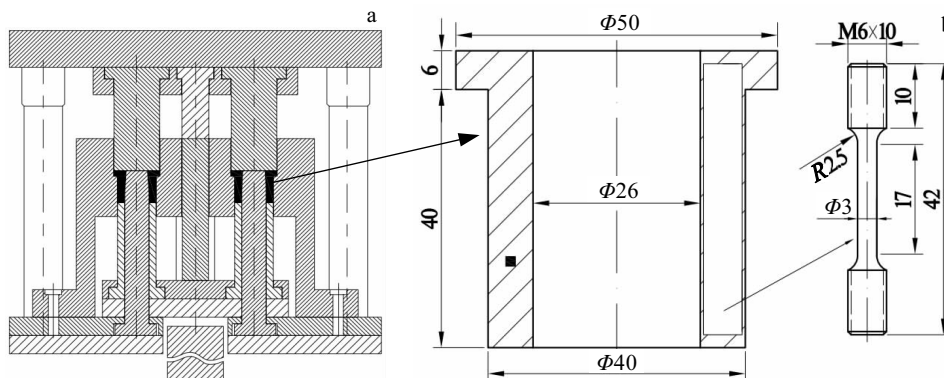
挤压模具和挤压零件尺寸及拉伸试样取样位置及尺寸
